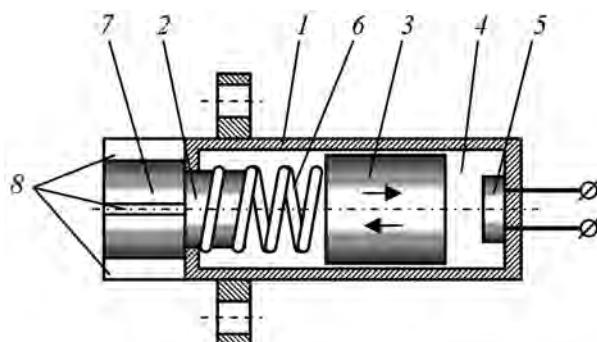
Пристрій для контролю температури оточуючого середовища [19]: 1 – порожнистий корпус; 2 – чутливий елемент; 3 – постійний магніт; 4 – порожнина корпуса 1; 5 – контакти магнітокерованого вимикача; 6 – пружина стиску; 7 – ділянка корпуса 1 для контакту з оточуючим середовищем.
